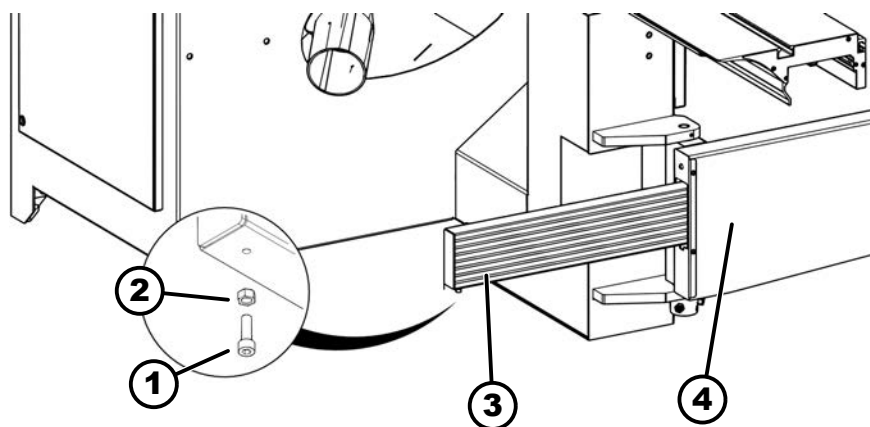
Monte el tubo deslizante en el brazo del carro escuadrador
